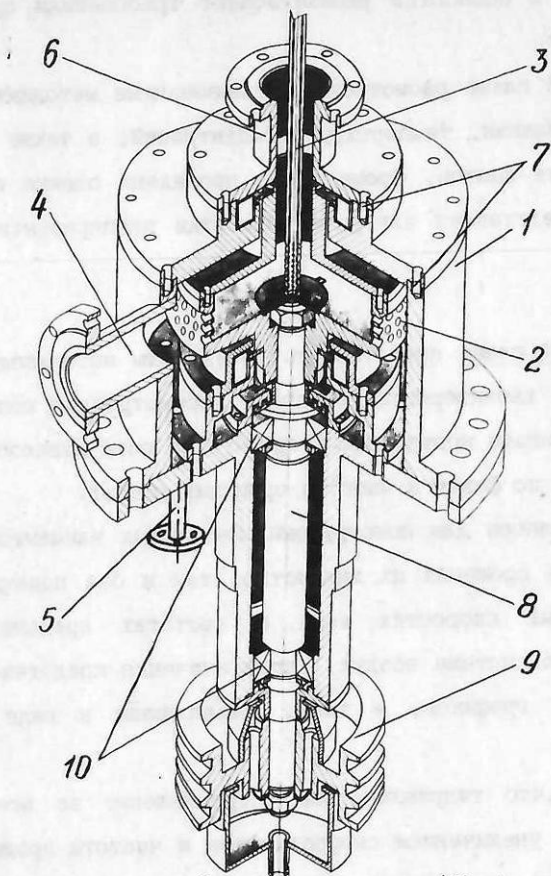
Конструкция высокоскоростного центробежного массообменного аппарата: 1- корпус; 2- перфорированная корзина ротора; 3- устройство подачи жидкости; 4- штуцер ввода газовой фазы; 5- сливной патрубкок; 6- осевая отводная труба (для выхода газа); 7- газонепроницаемые уплотнения импеллерного типа; 8- вал; 9- шкив клиноременной передачи; 10 - подшипниковые узлы.
